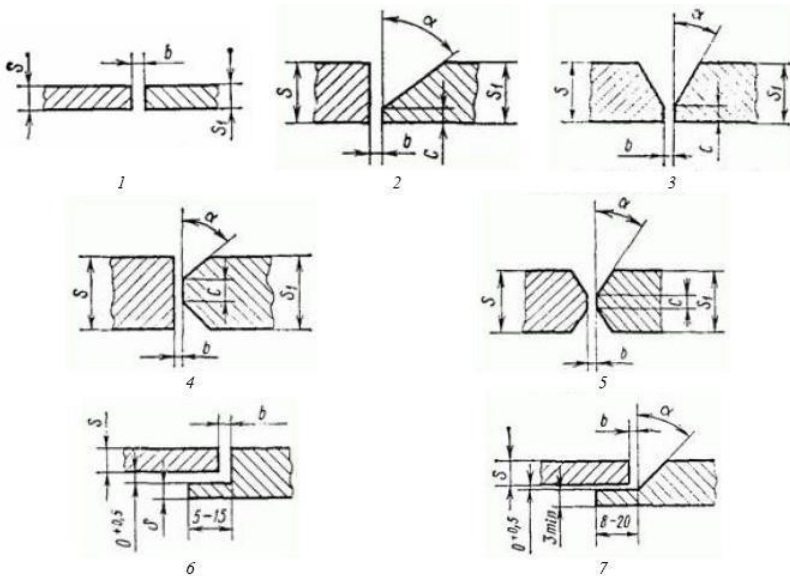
Конструктивні елементи підготовки кромки до зварювання:
